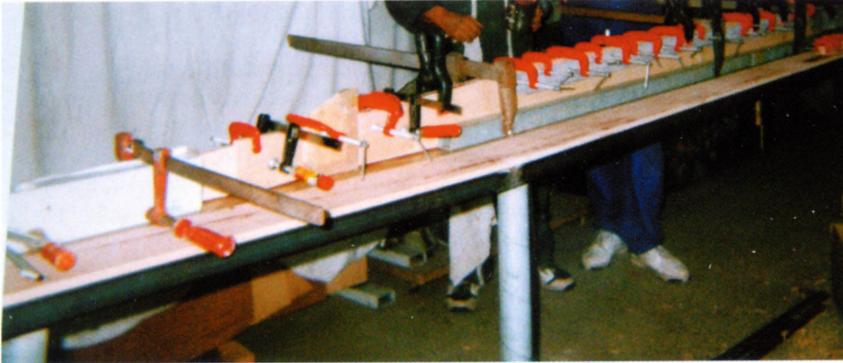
Fabrication des semelles en lamellé – collé en forme, sur le moule.
